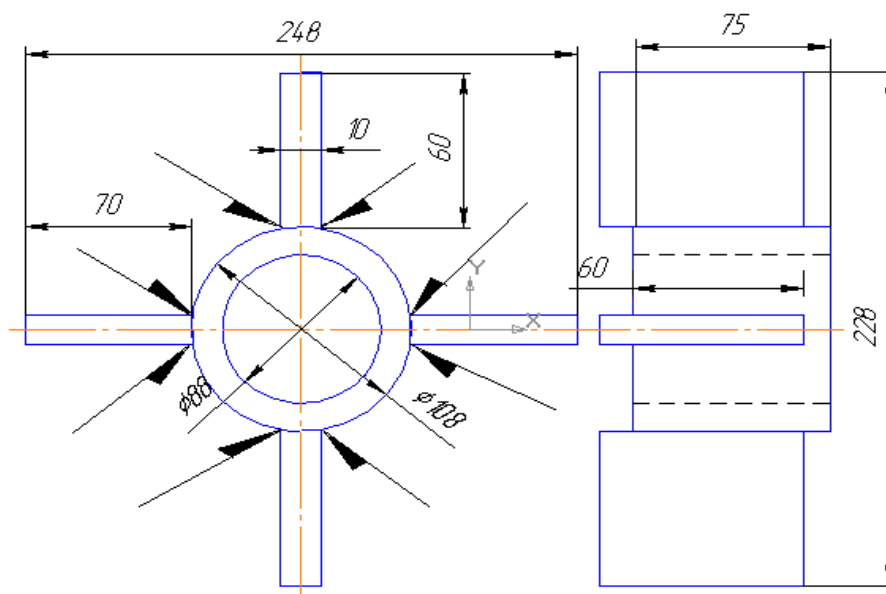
Изготовление втулки надрессорной балки тележки пассажирского вагона
